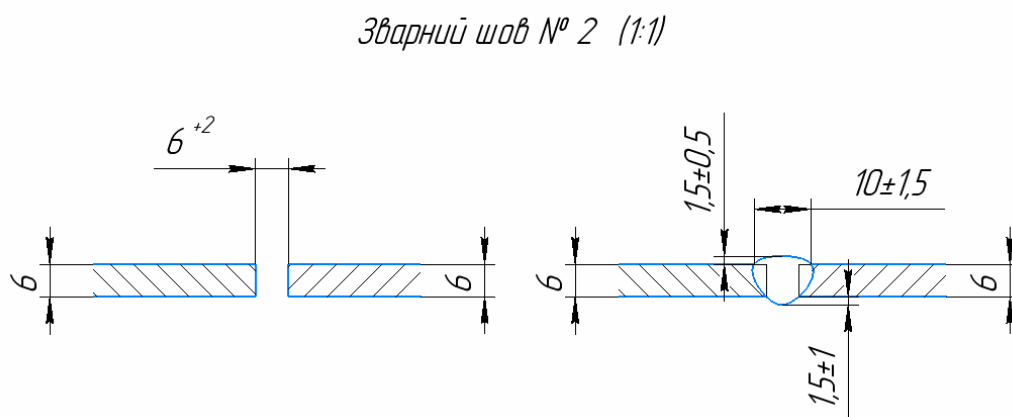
Схема підготовки до зварювання та зварного шву №2
